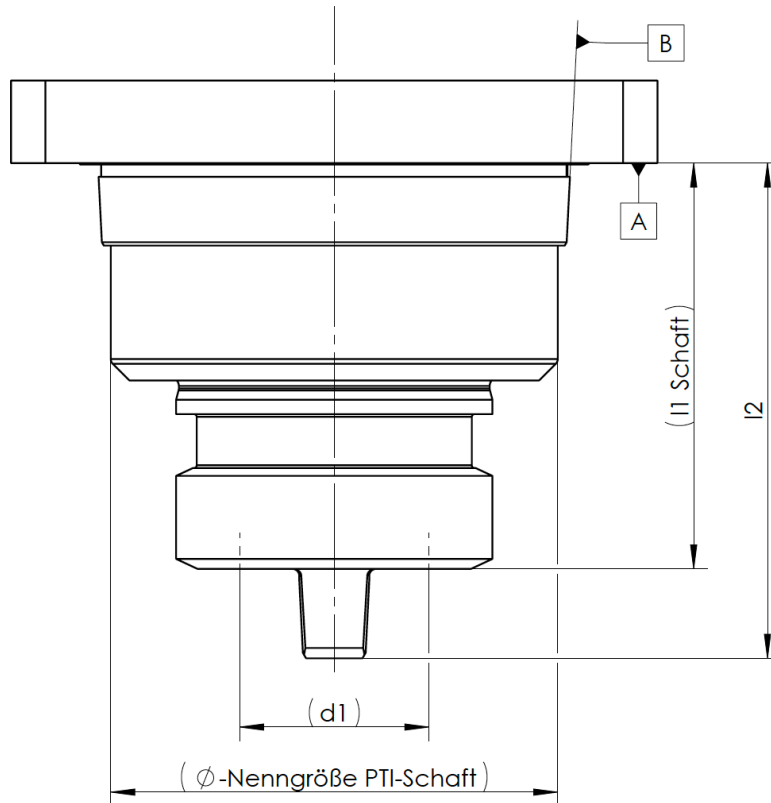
PTI-Kupplung für angetriebene PTI-Werkzeuge
